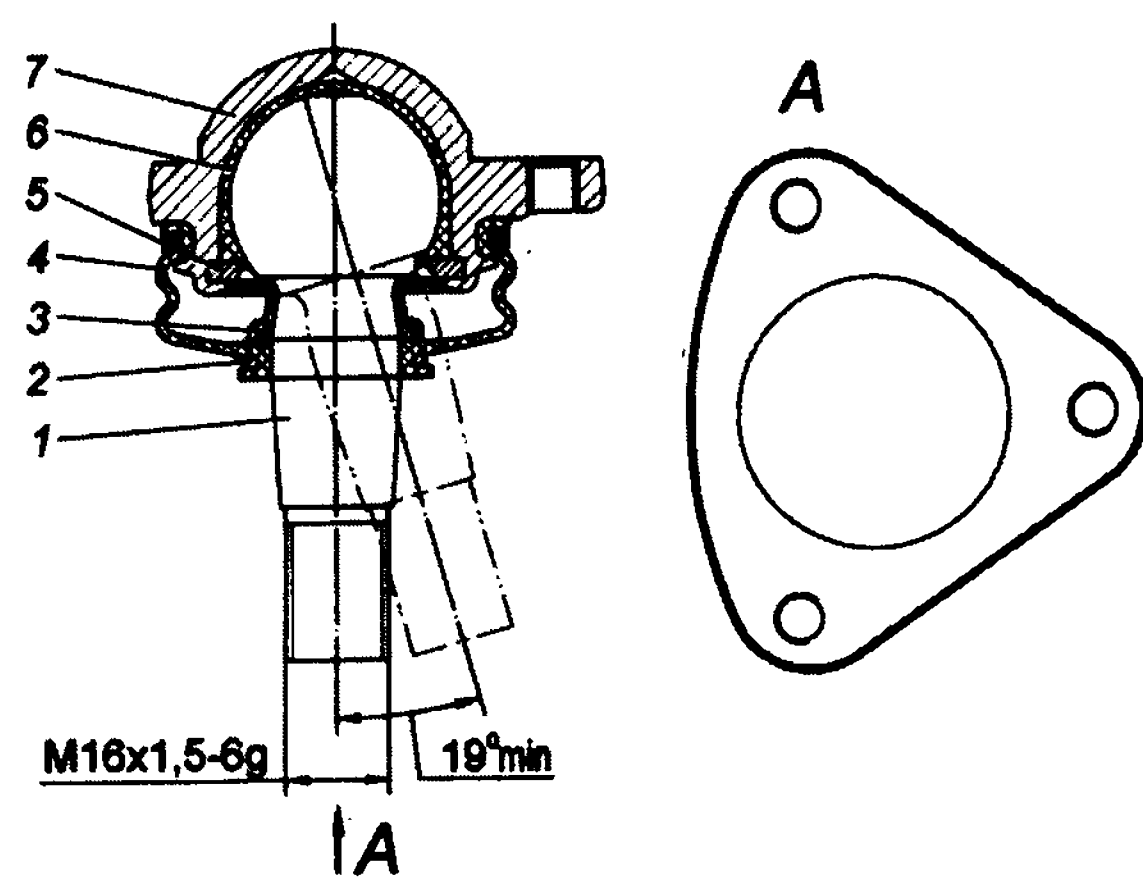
Шаровой шарнир: 1 — шаровой палец; 2 — пружинное кольцо; 3 — втулка распорная; 4 — уплотнитель; 5 — шайба ограничительная; 6 — вкладыш; 7 — корпус шарнира
